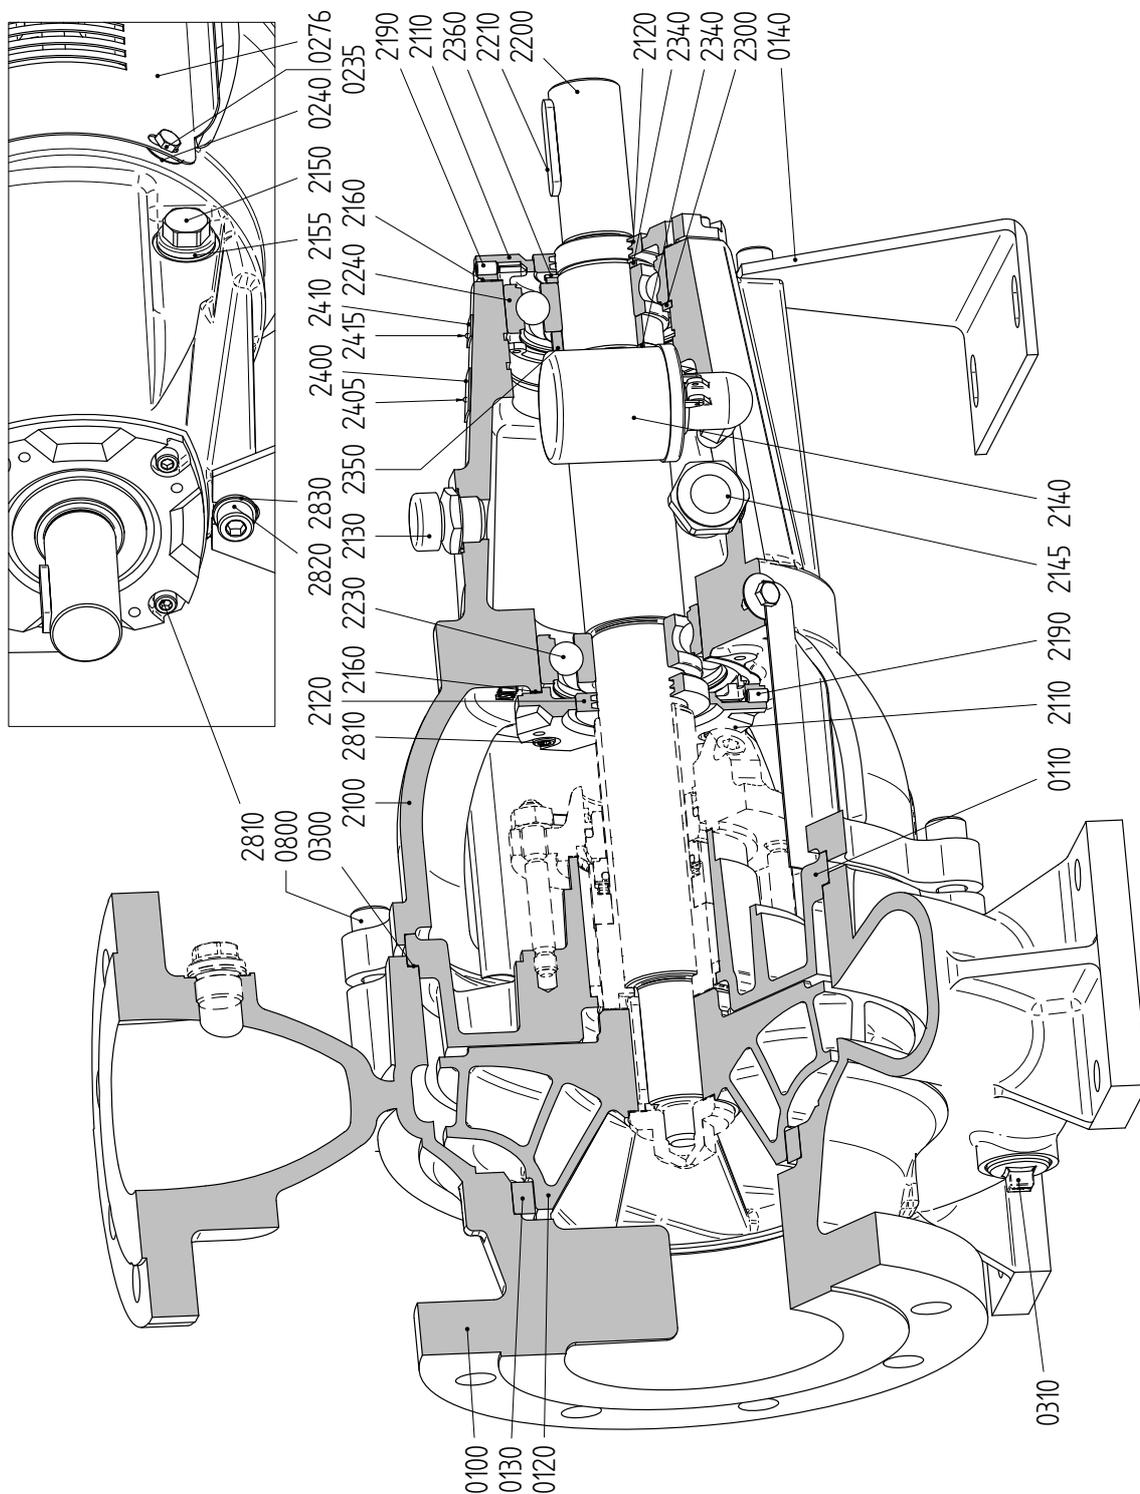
Schéma en coupe L3 - groupes de palier 1, 2, 3.
